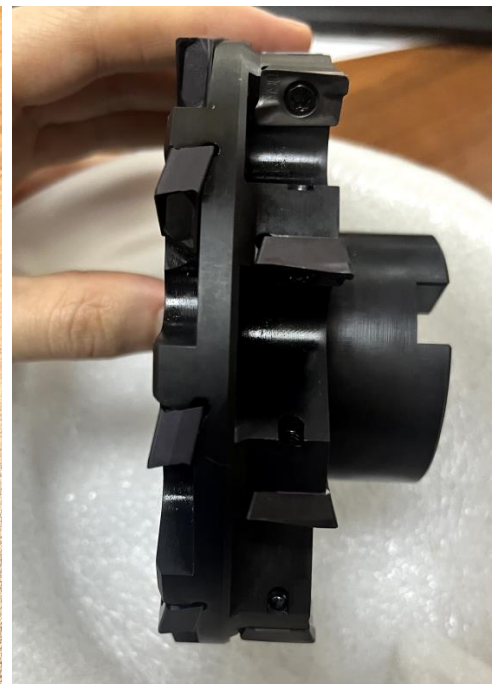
Опытный образец дисковой фрезы с СМП.
